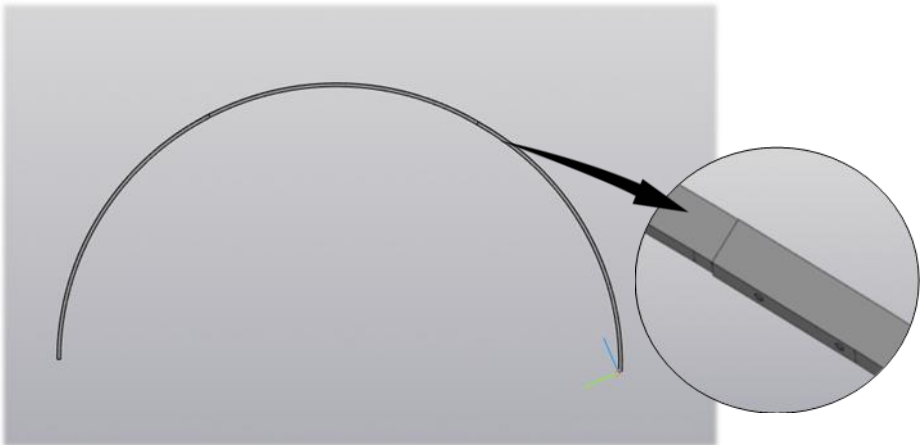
Схема сборки торцевых дуг теплицы
